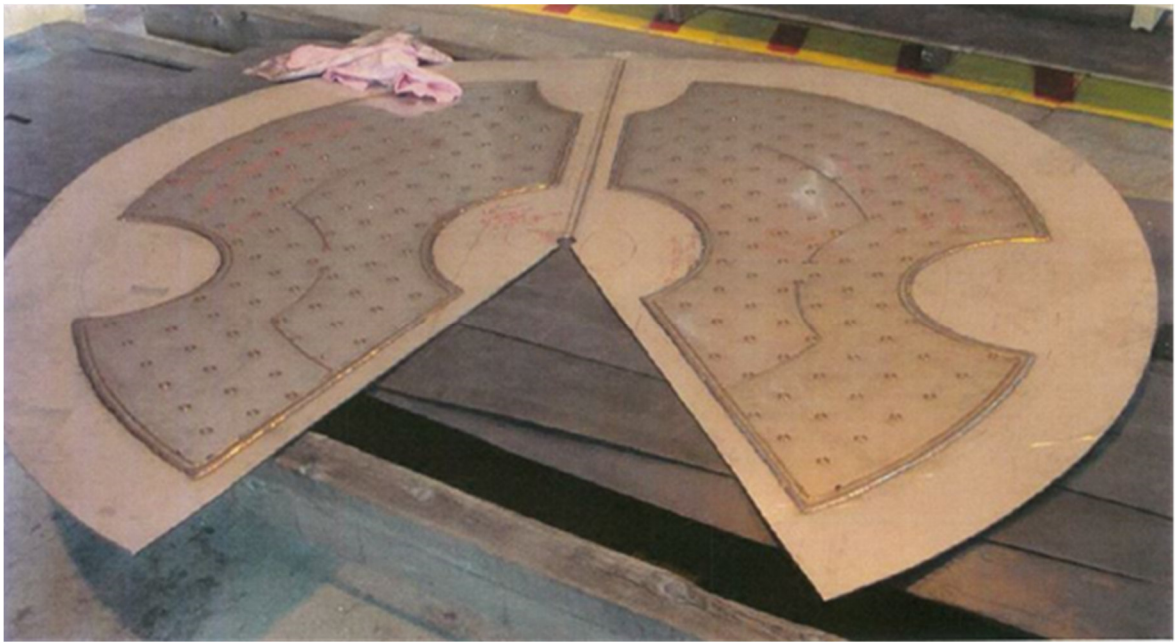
Lasergeschweißtes Blech<sup>15</sup>
